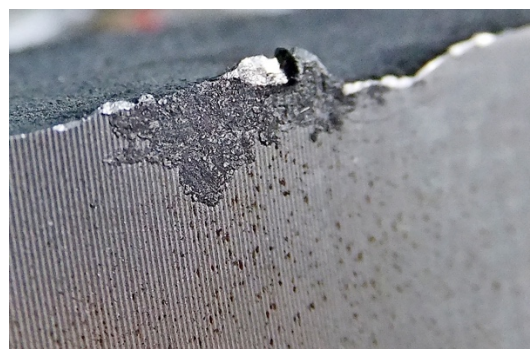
Участки излома корпуса, разрушившегося в ходе эксплуатации
